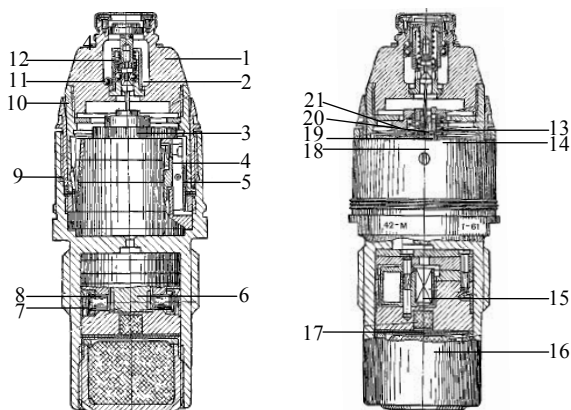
Дистанційний підривник В-90: 1 – головна втулка; 2 – гільза; 3 – стріла; 4 – пусковий стопор; 5 – фіксувальне кільце; 6 – поворотна втулка; 7 – пружина; 8 – центробіжний стопор; 9 – ніж; 10 – втулка; 11 – кулька; 12 – запобіжна пружина; 13 – кільце; 14 – пружина; 15 – капсюль-детонатор; 16 – шашка; 17 – передаточний заряд; 18 – пружина; 19 – жало; 20 – кулька; 21 – установлювальна планка
